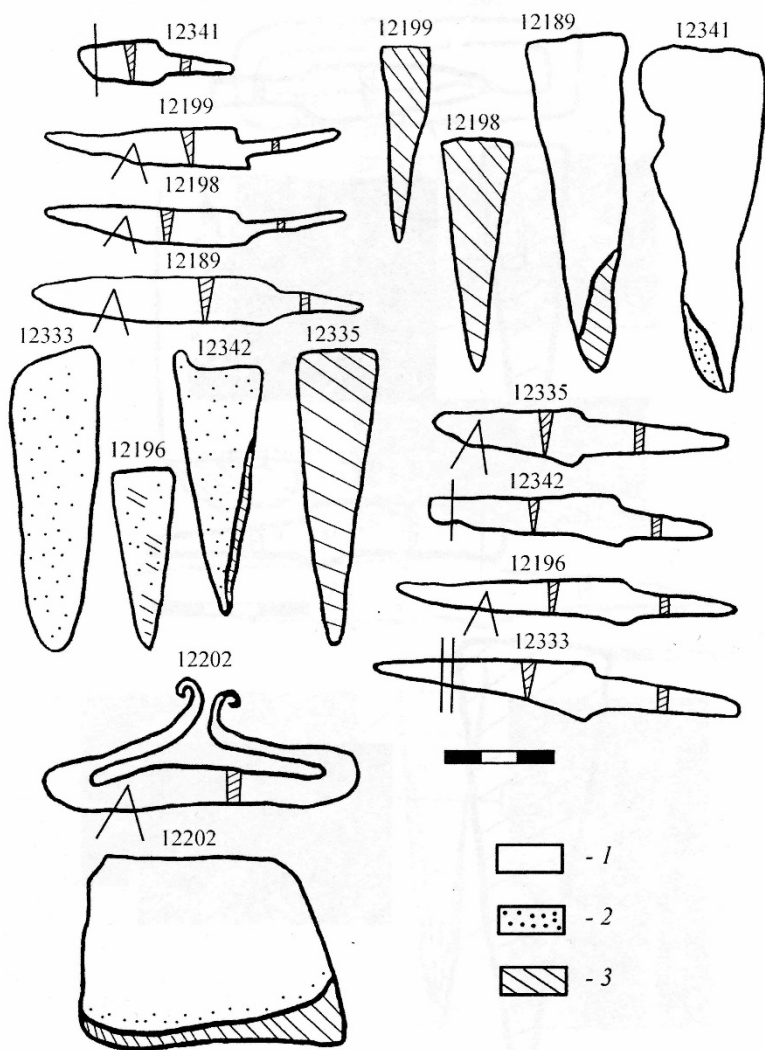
Технологические схемы изготовления ножей и кресала из Истье 2.
